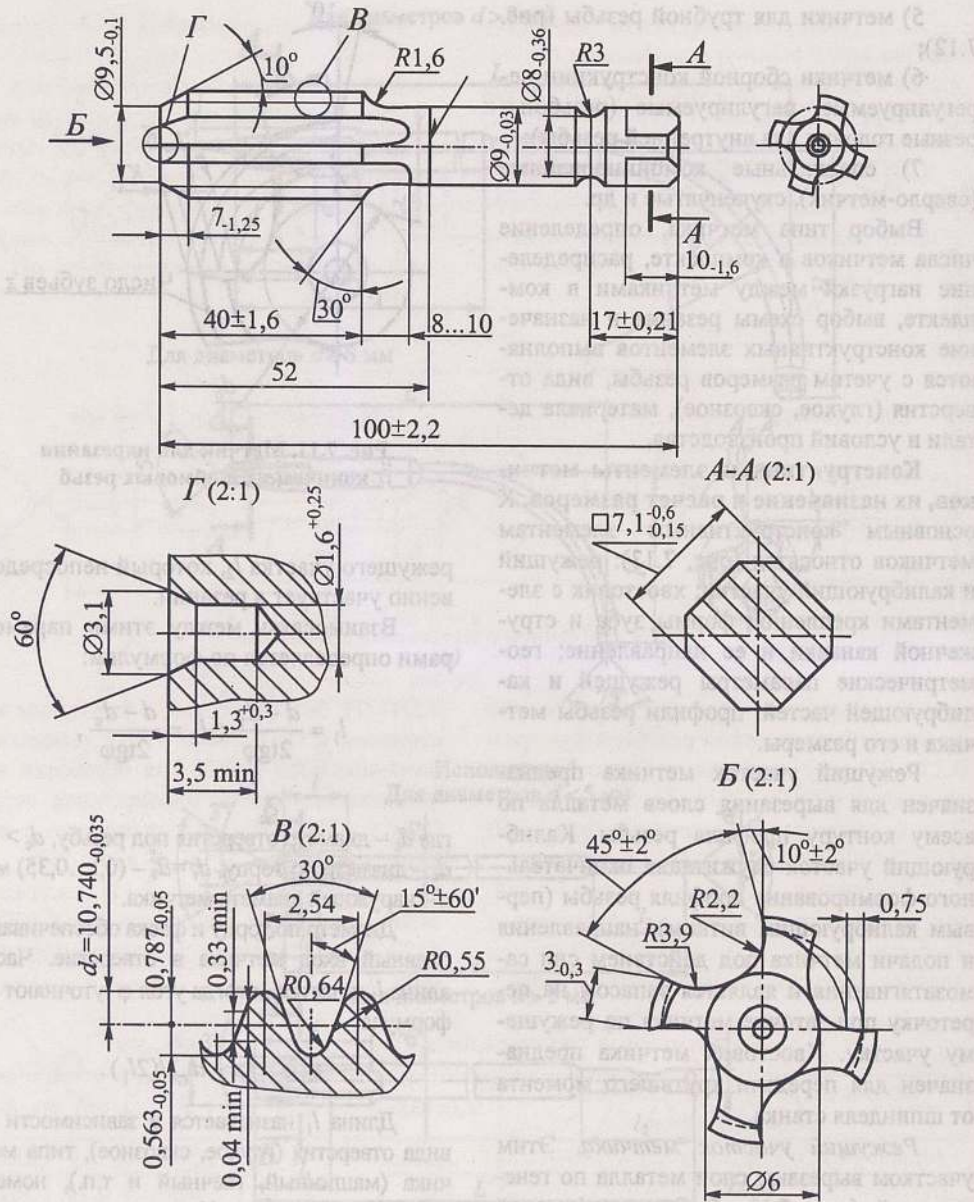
Конструкция и размеры метчика для трубной резьбы
